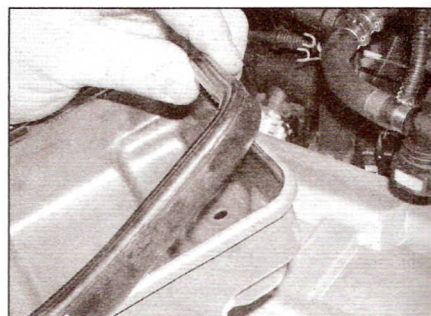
Надлежащим образом установите резиновый уплотнитель на крышку головки цилиндров
